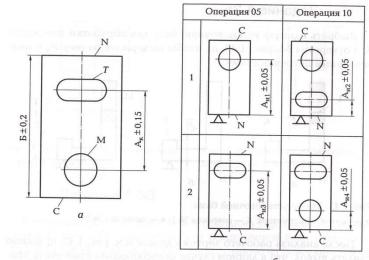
Последовательность обработки поверхностей: a — чертеж конструктора; b — варианты (1 и 2) последовательности обработки
